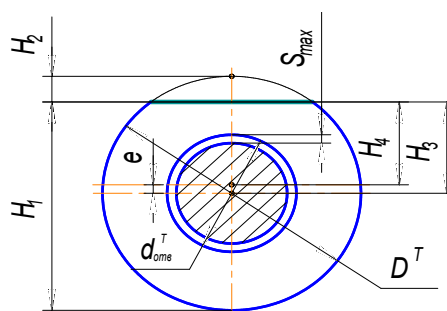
Схема установки заготовки на горизонтальный установочный палец
